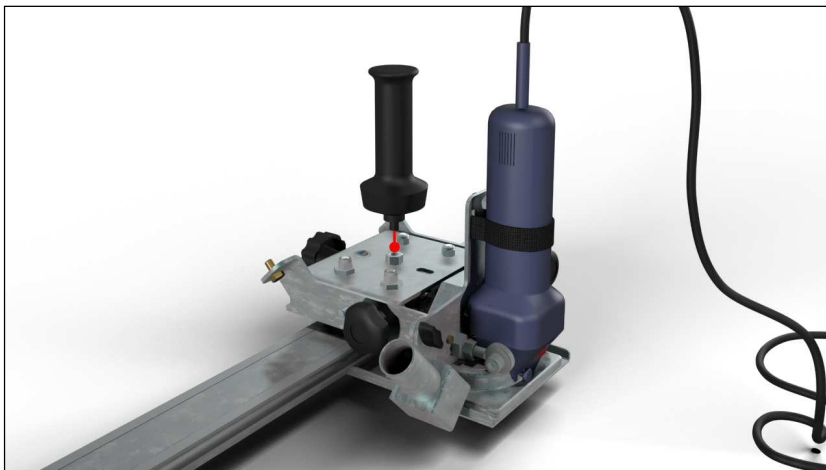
Molette de blocage du réglage millimétrique.
